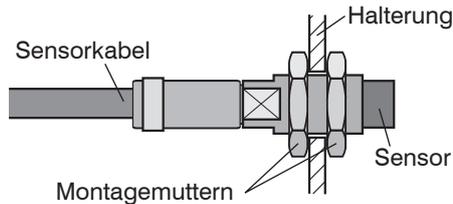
Ungeschirmter Sensor mit Gewinde in Standardmontage
